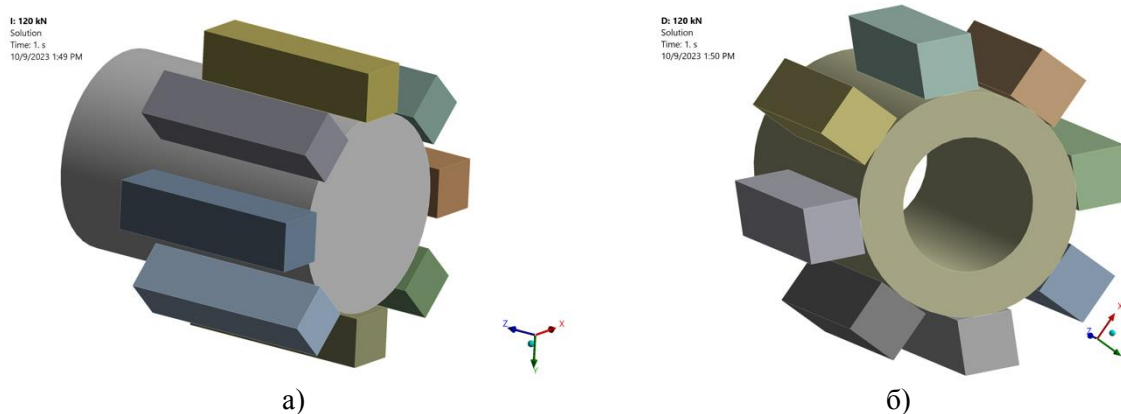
Solid-моделі ковпачка з обтискними елементами преса:
